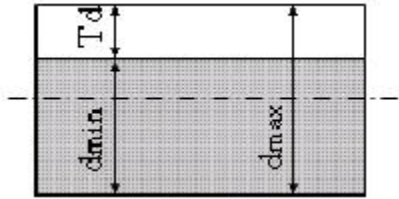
Предпочтительное изображение вала, Td – допуск на диаметр вала
